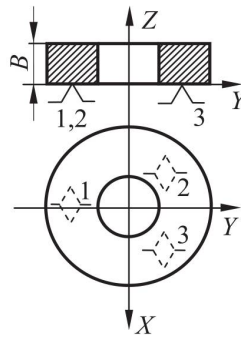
Установка заготовки з позбавленням трьох ступенів свободи
